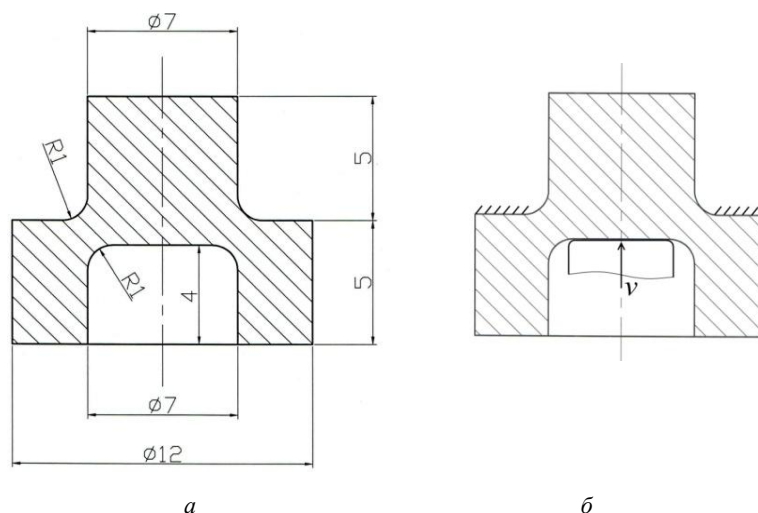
Эскиз образца «колокольчик» для испытаний на растяжение (а) и схема приложения нагрузок (б)
